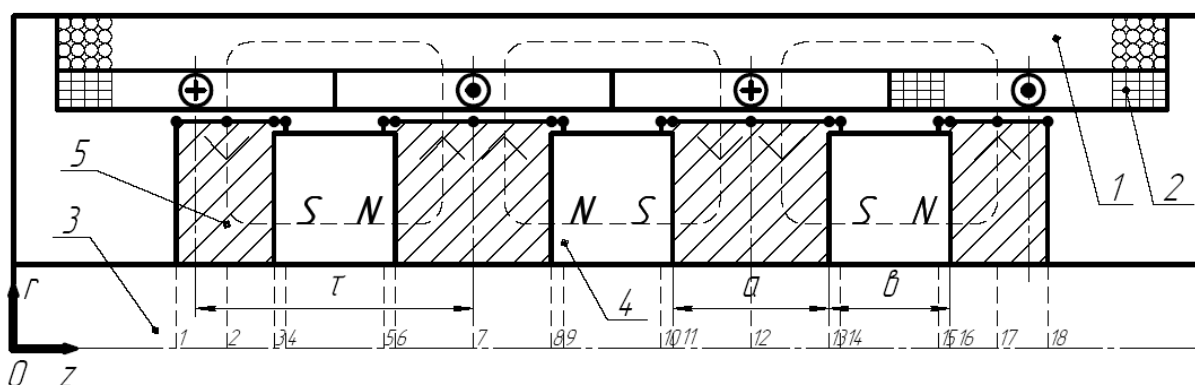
Схематическое изображение конструкции линейного двигателя с ПМ:
